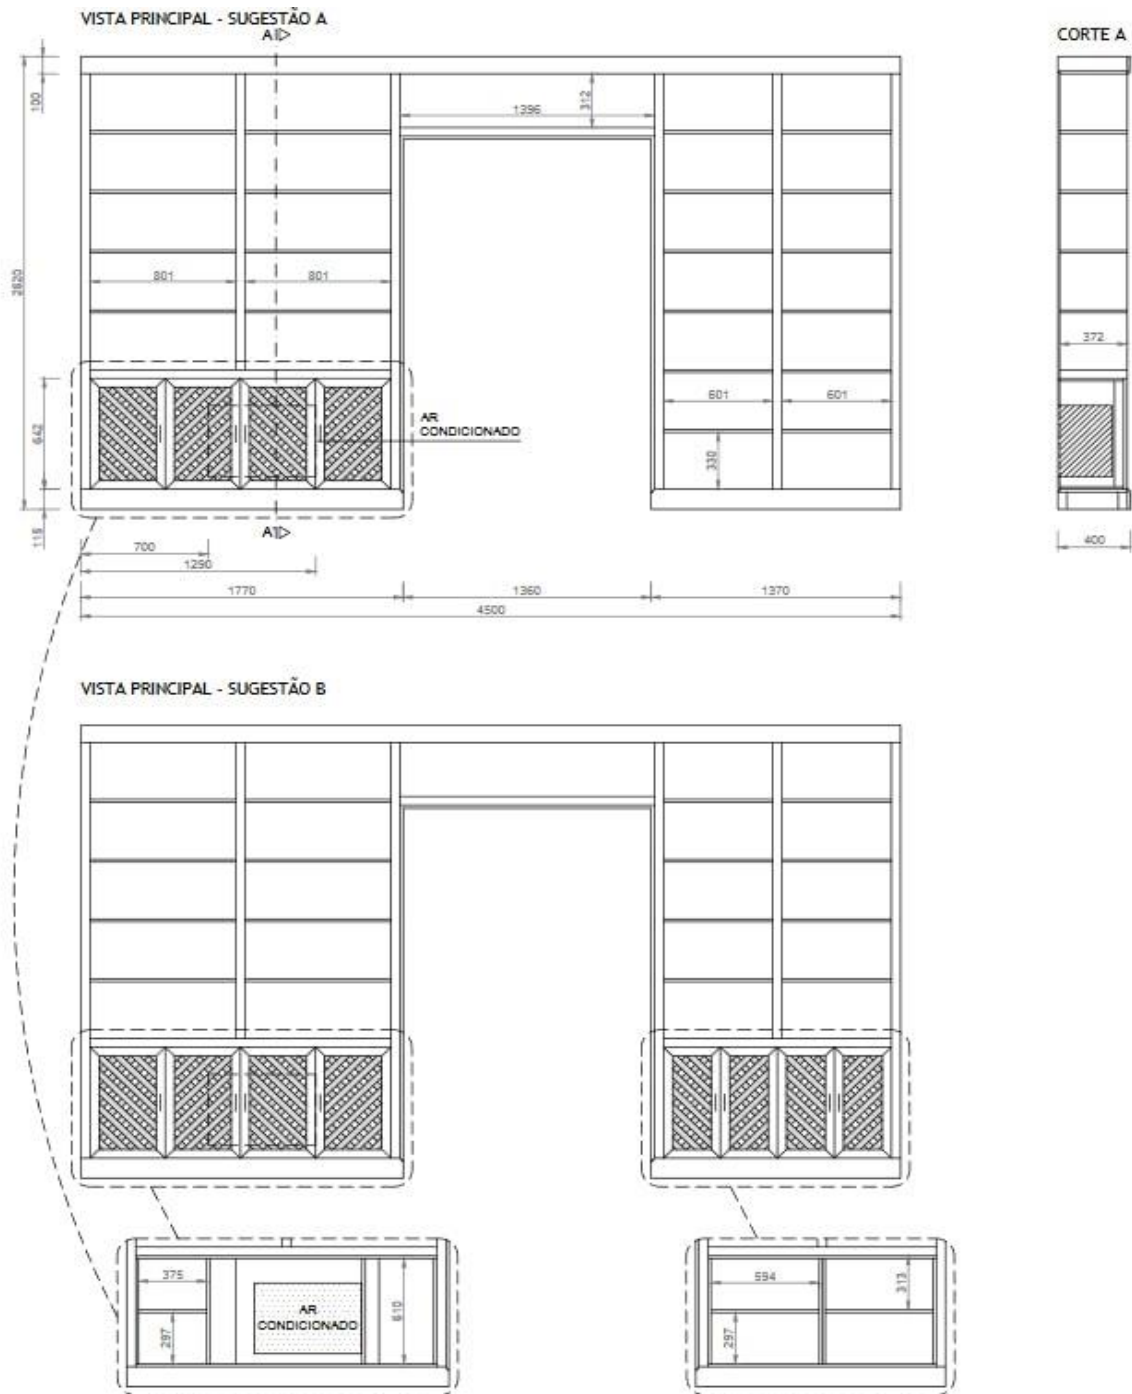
Proposta "A" e "B". Desenho técnico. Cotagem geral do equipamento.
